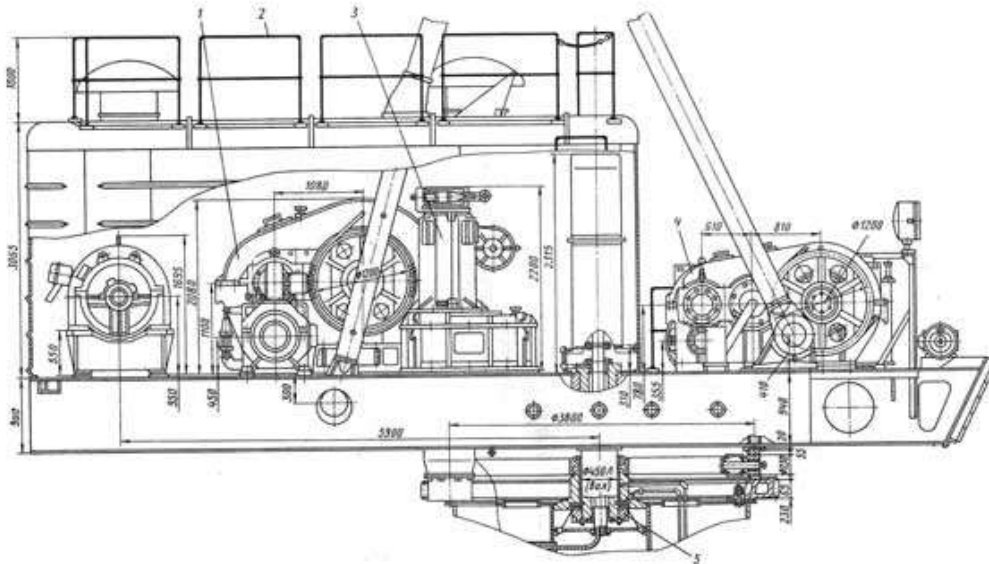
Схема розташування обладнання на поворотній платформі.
